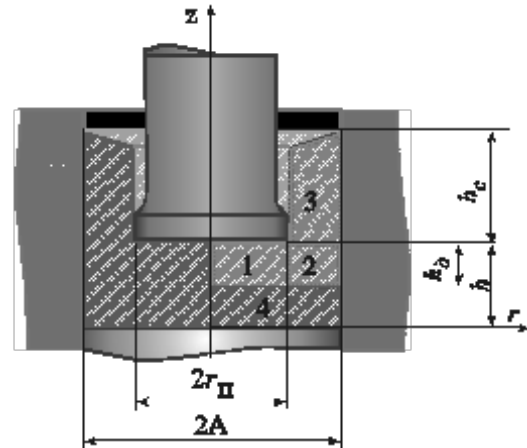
Схема выдавливания детали и разбивки заготовки на зоны
